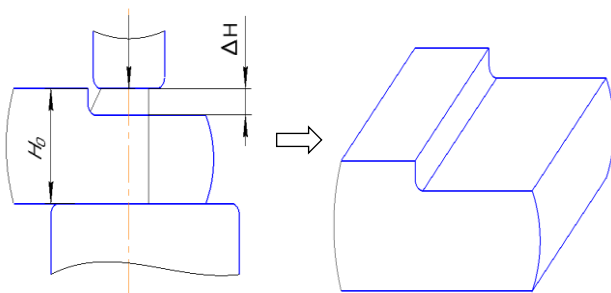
Схема получения одностороннего уступа для призматических заготовок
